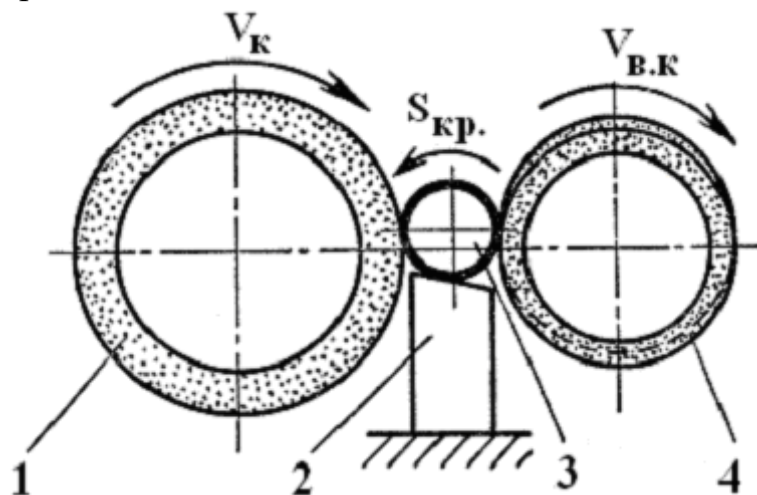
Обработка заготовок на бесцентрово-шлифовальных станках:
